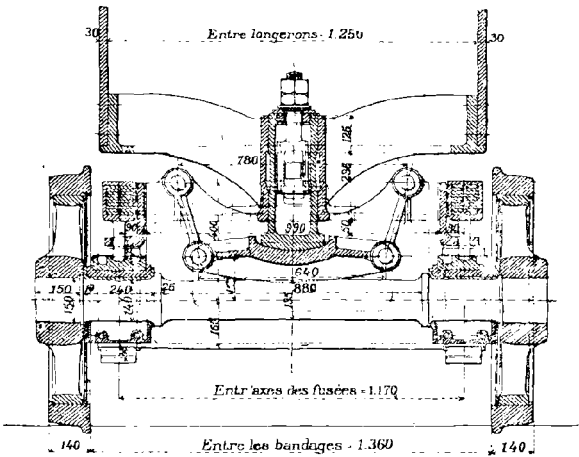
bis. — Bissel des machines 4000 de la Compagnie du Midi.
